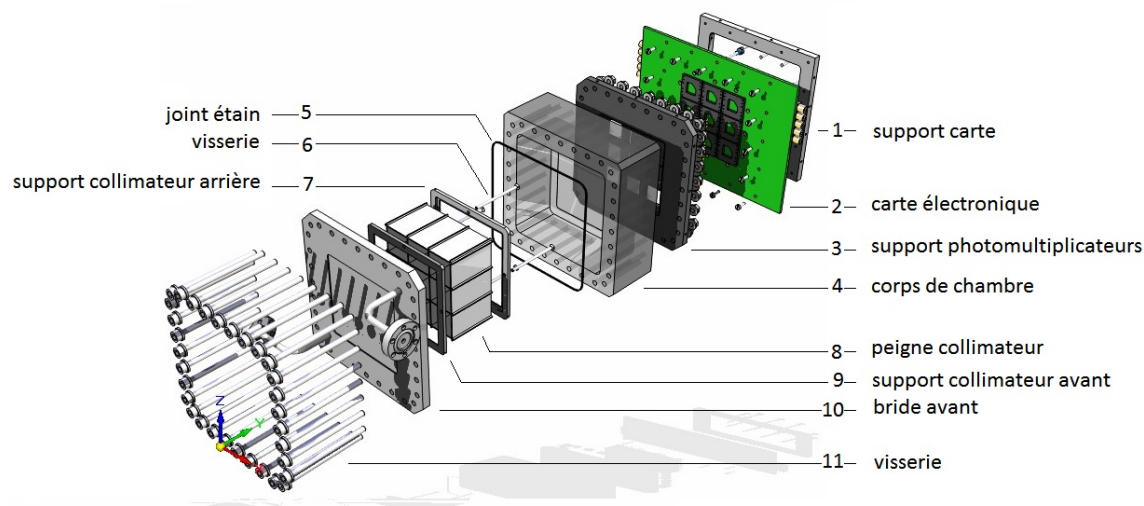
Vue en éclaté de l'ensemble des pièces constitutives du démonstrateur optique.
